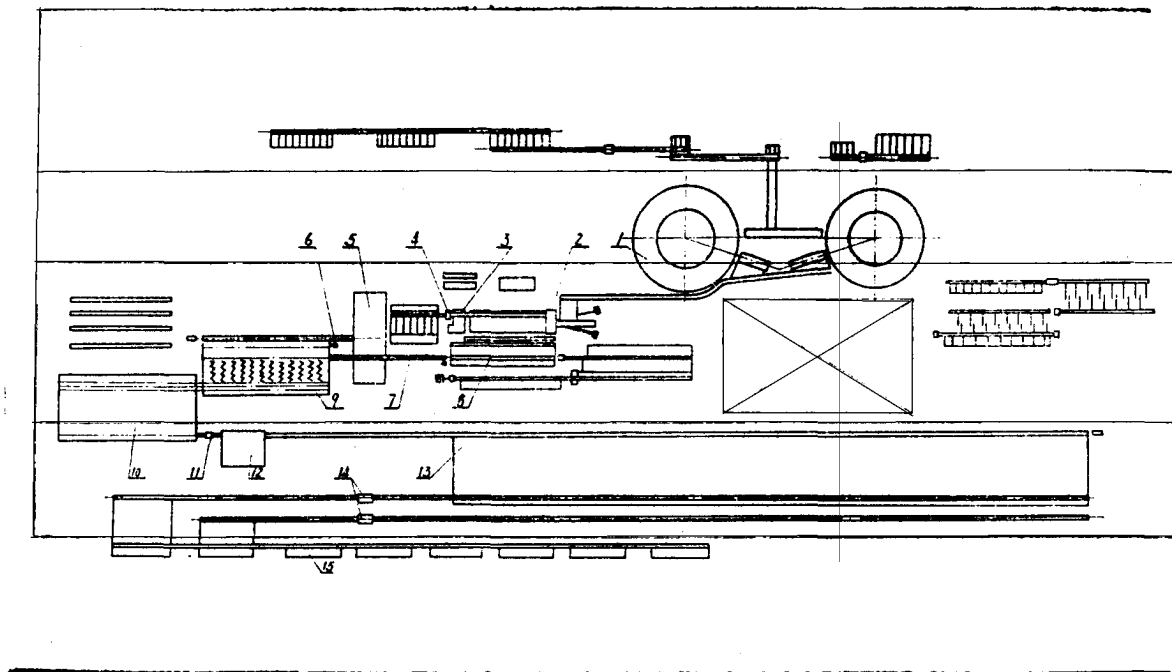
波兰耶德那斯厂连轧管机组平面布置图
